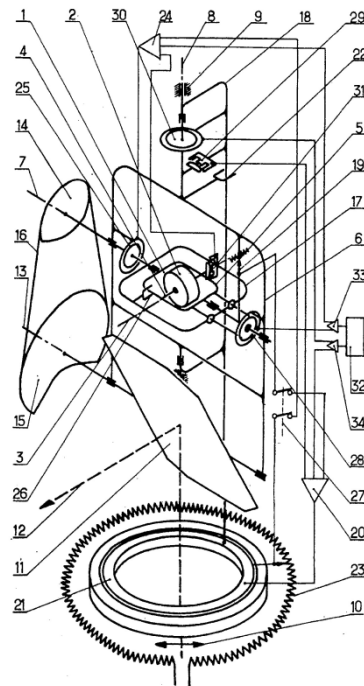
Схема кінематична вузла передачі руху: 1 – сектор, 2 – паразитне колесо, 3,4- металеві стрічки
